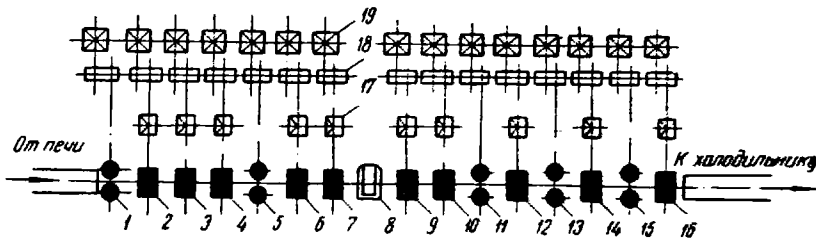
Схема расположения оборудования непрерывного стана 350:
